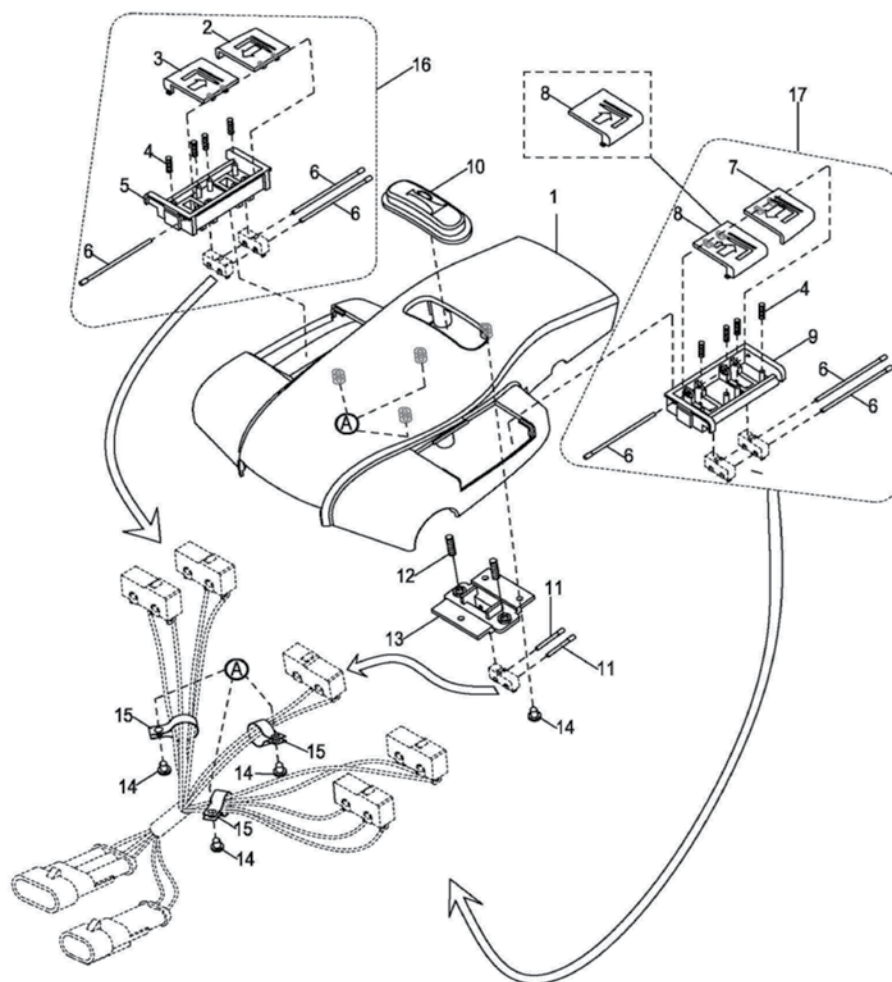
ASSEMBLAGE DE GAUCHE MONTER ET DESCENDRE
